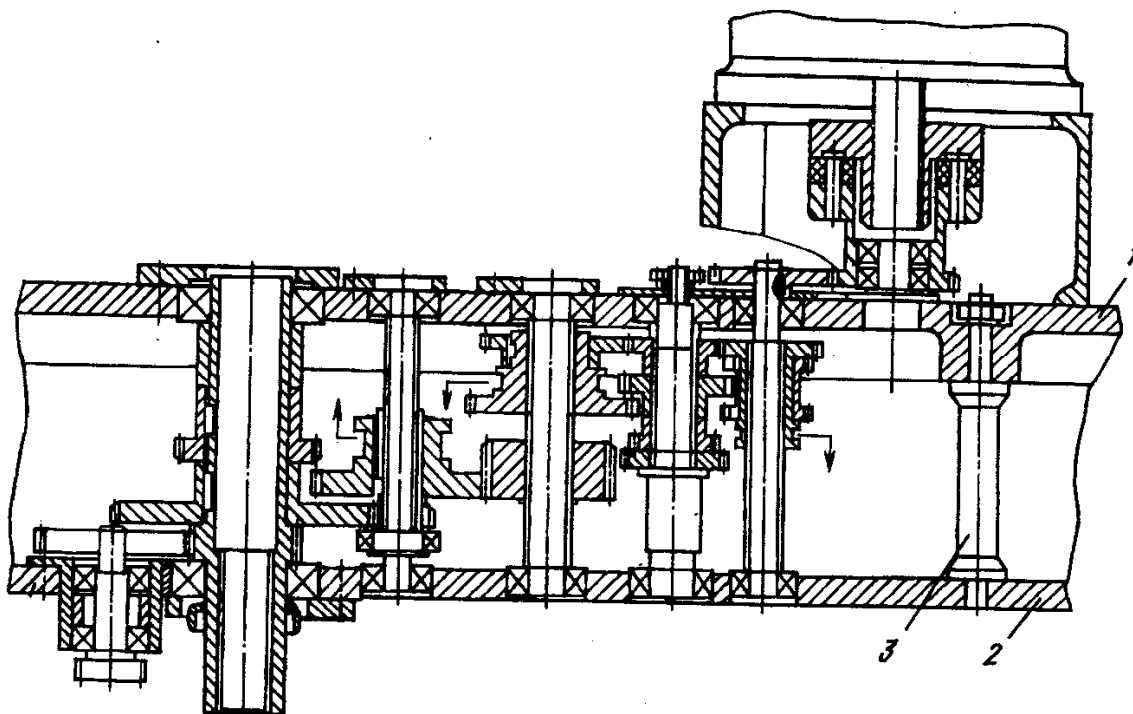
Коробка скоростей станка мод. 2Н135.
